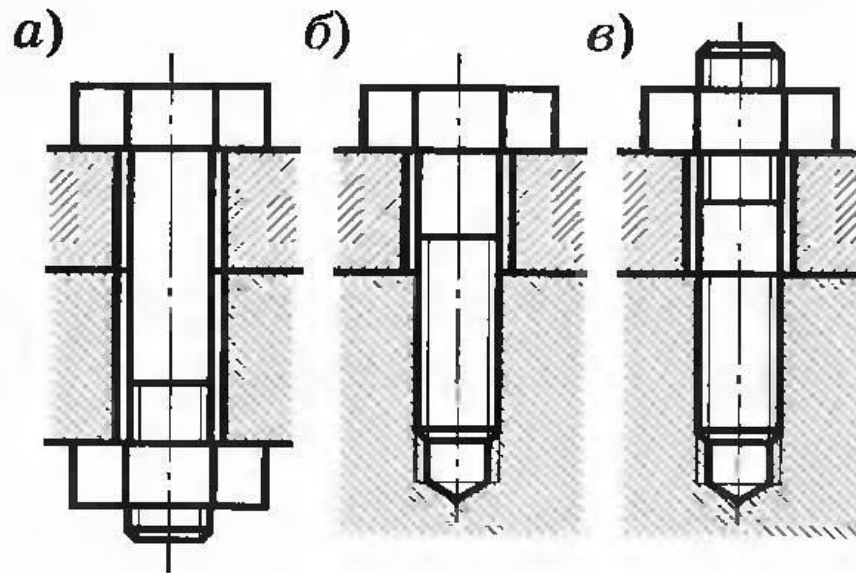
Виды резьбовых соединений: *a* — болтовое; *б* — винтовое; *в* — шпилечное
